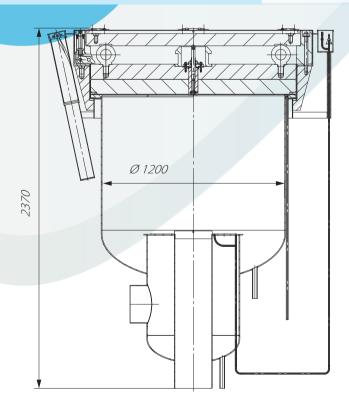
Общий вид камеры фильтра ФАРТОС-3500 РЕ 722.00.00.000.
